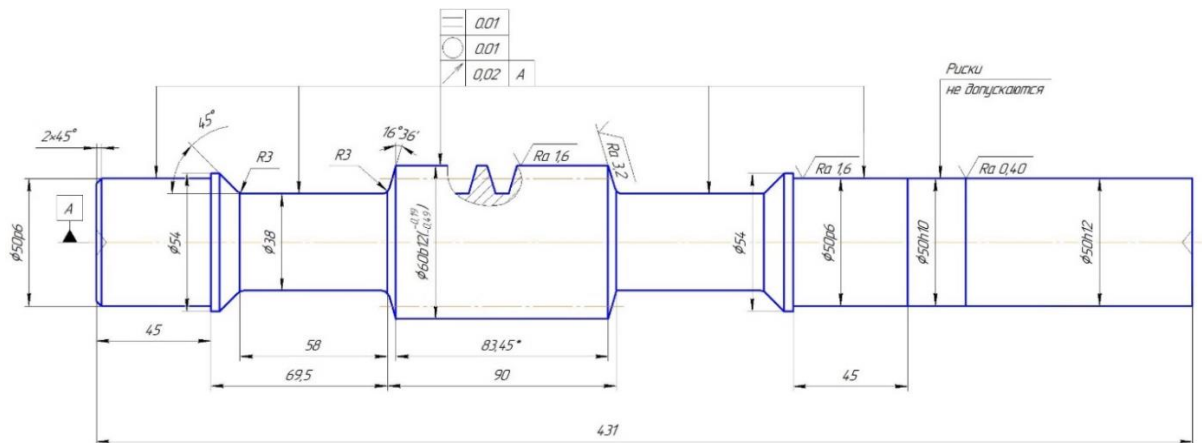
Ескіз обробки поверхонь на операції Токарна з ЧПК
